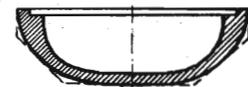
Sezione dello scafo dopo l'arrotondamento.
